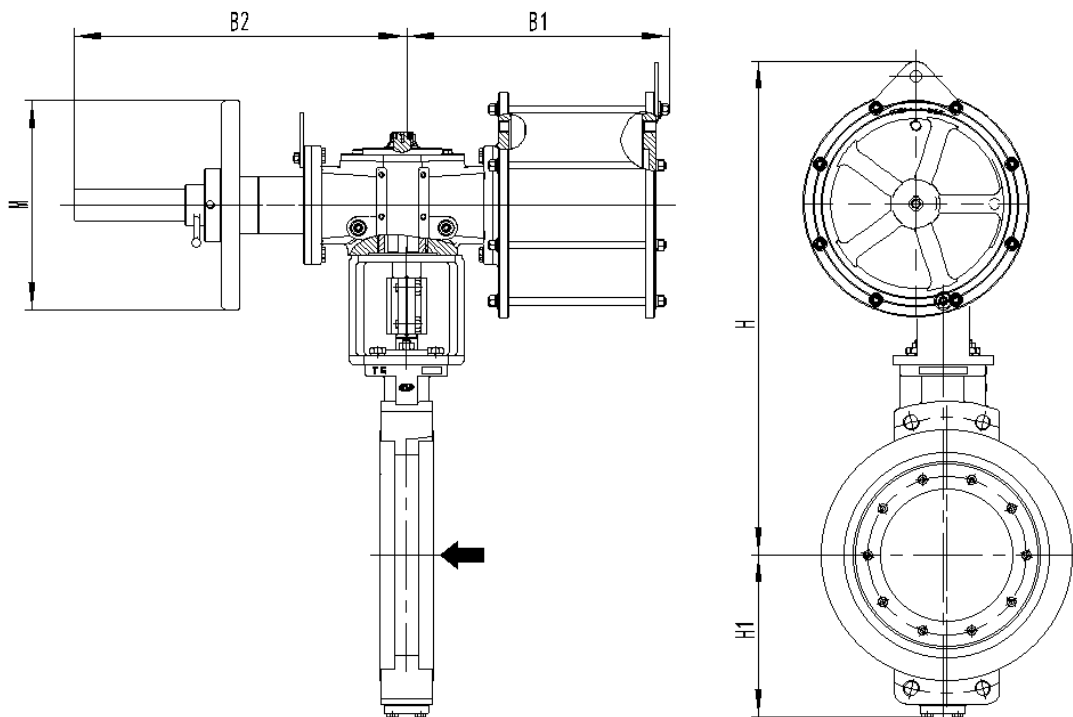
配 AW18D001~AW27D002 带丝杆手轮外形尺寸图
